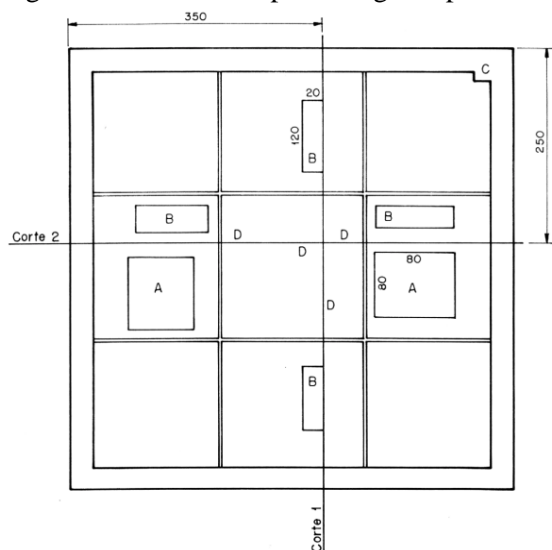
Fôrma metálica utilizada para fabricação das placas de gesso.
